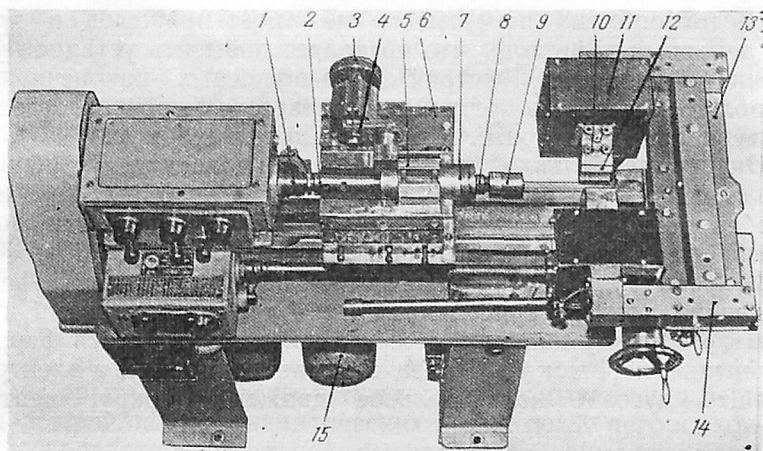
Общий вид токарно-винторезного станка мод. ТВ-4 с устройством для магнитно-абразивной обработки мод. ЭУ-1
